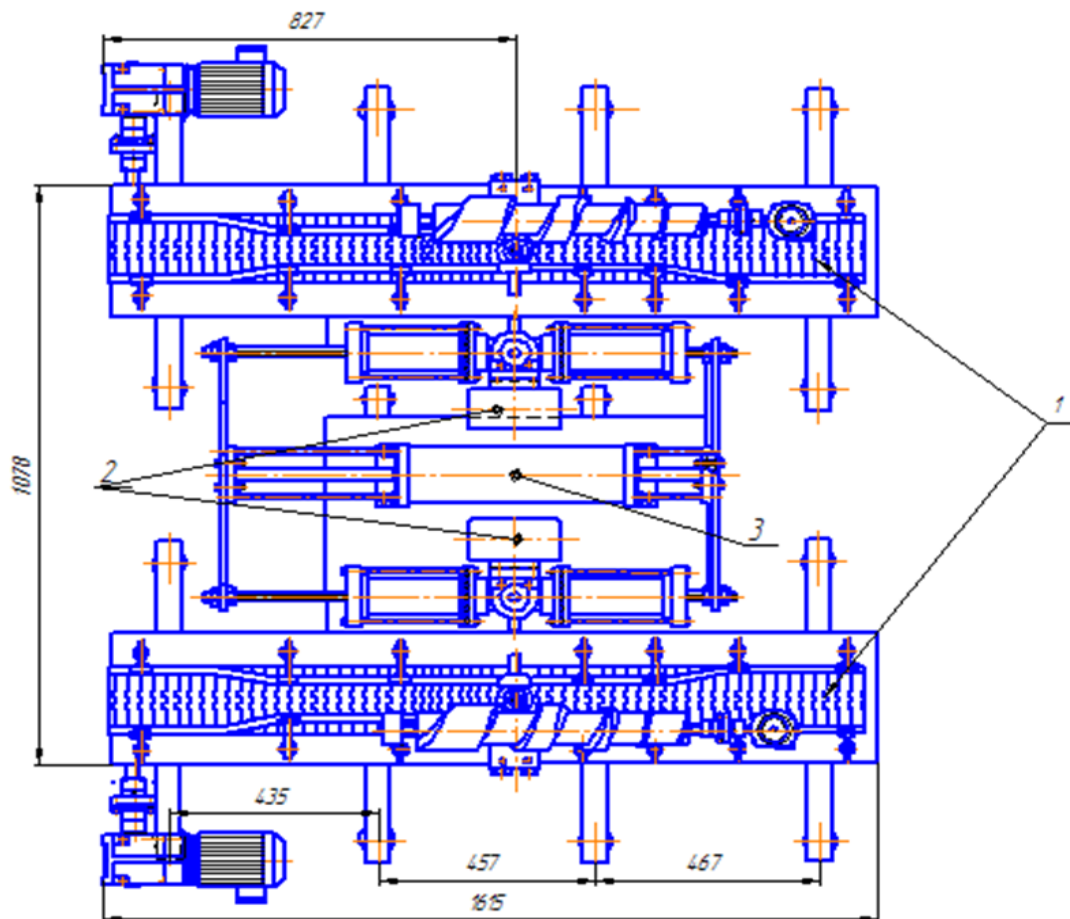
Загальний вигляд машини для фасування в'язкої продукції в споживчу тару: 1- пластинчастий конвеєр; 2- поворотній пневмоциліндр; 3- пневмоциліндр із прохідним штоком.
